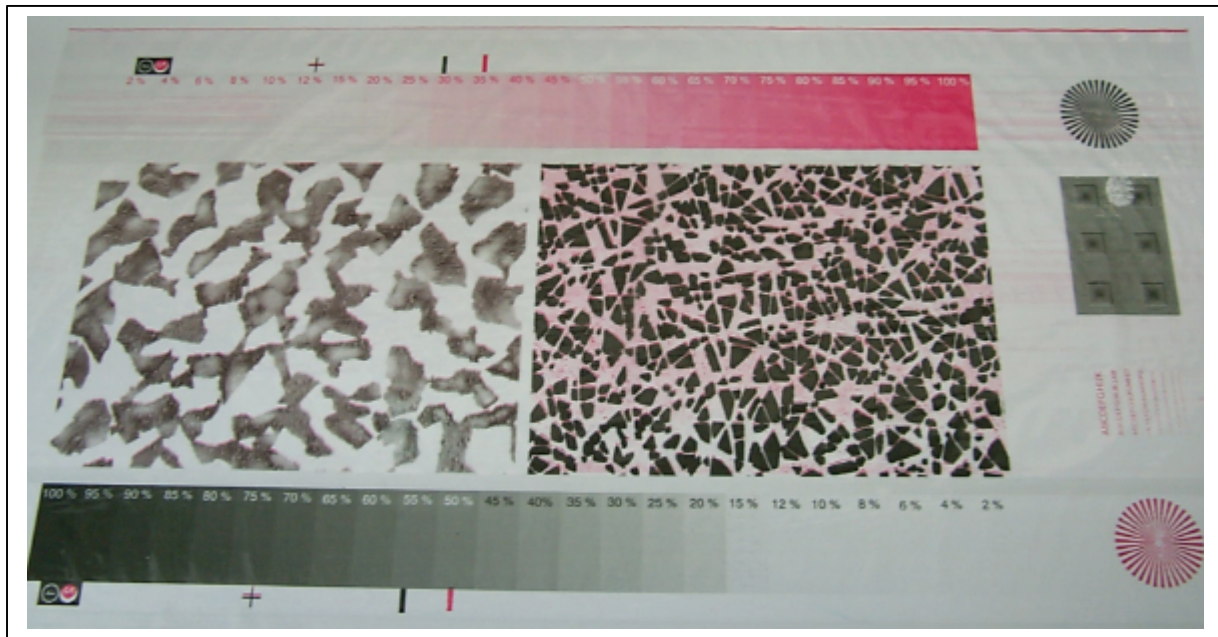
Druckbild auf Polyethylen, das mit einer Testdruckform erzeugt wurde
